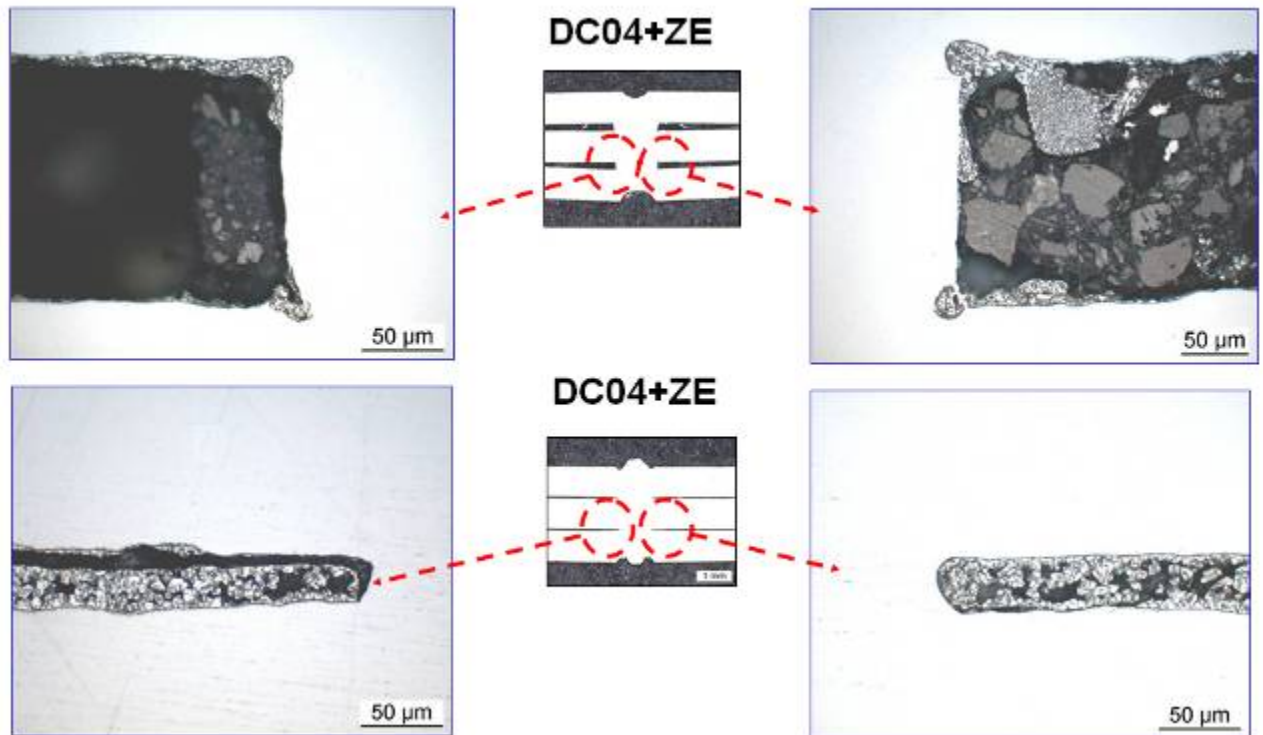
Querschliffe der Schweißverbindungen, Werkstoff: DC04+ZE
